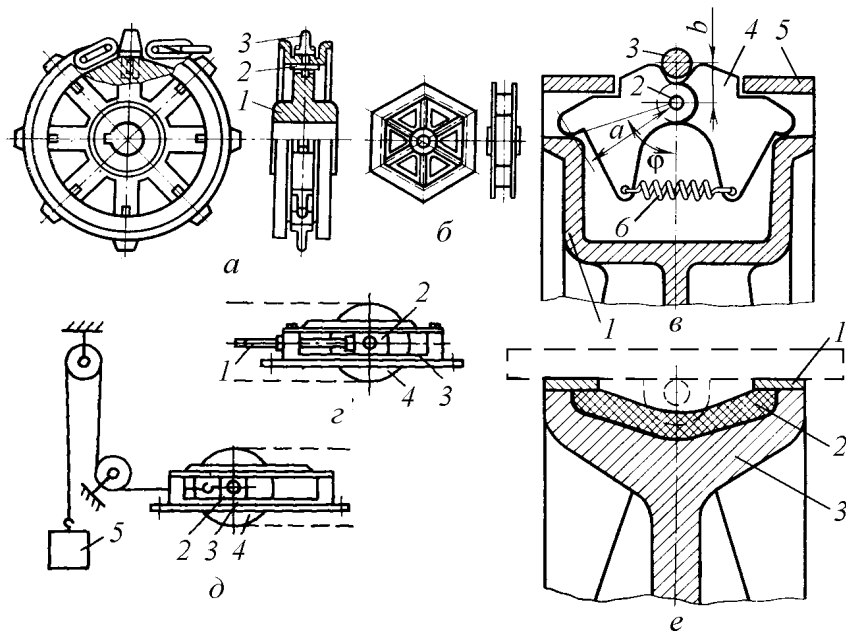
Ведущие звездочки и колеса: *а* – для цепи из круглой стали; *б* – для пластинчатой цепи; *в* – канатоведущий шкив с зажимными устройствами; *г* – винтовое натяжное устройство;
